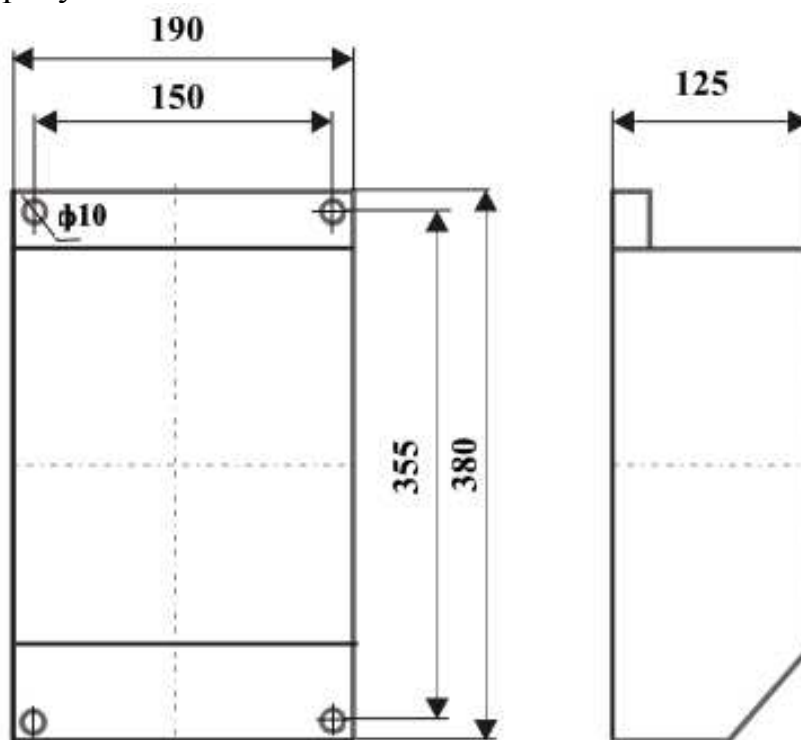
Габаритный чертеж преобразователя SDC1-47
